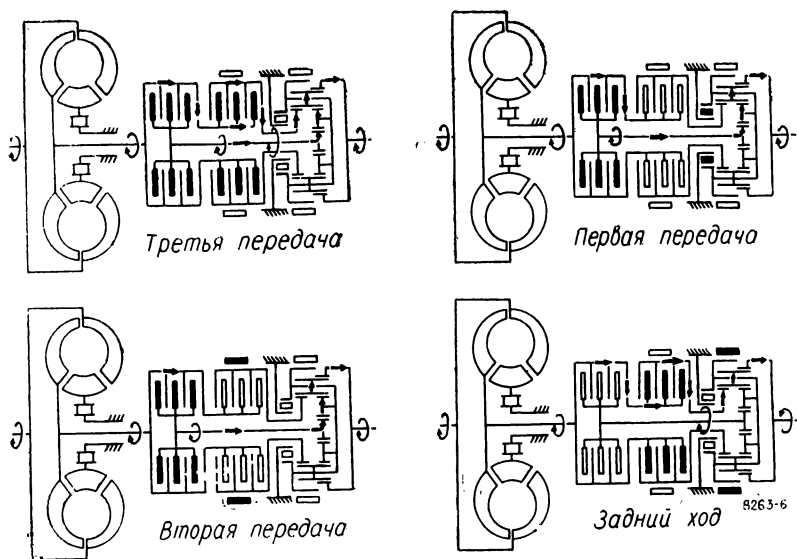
Схема включений сцеплений и тормозов при работе автоматической коробки передач
